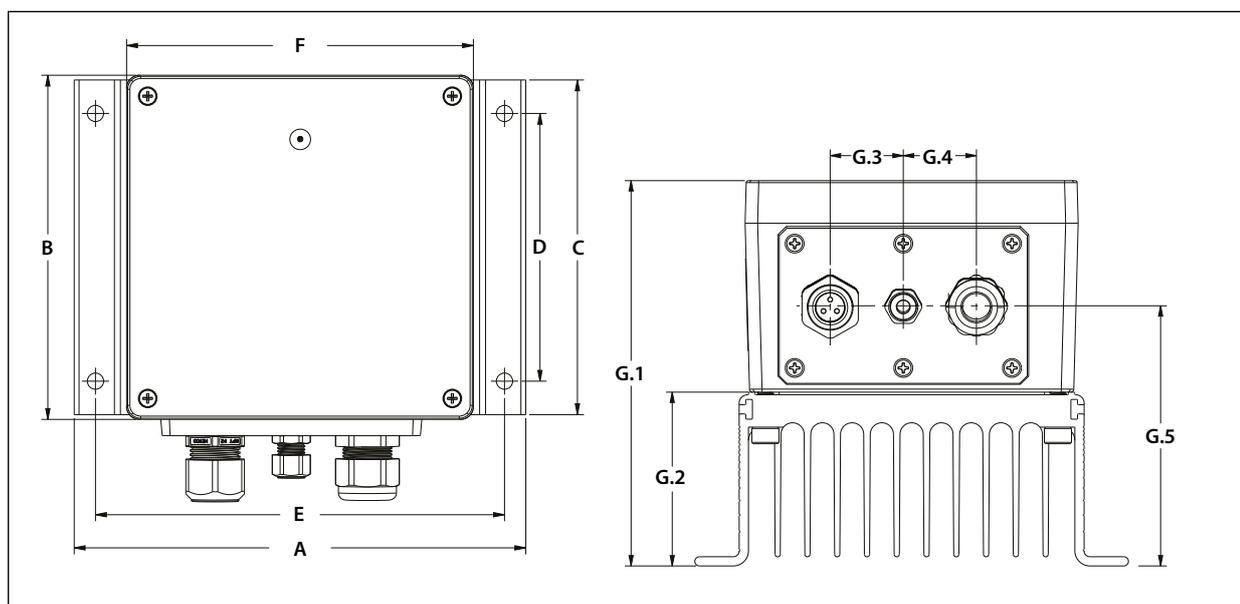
Dimensionais do Conversor AC/DC Solar Drive
